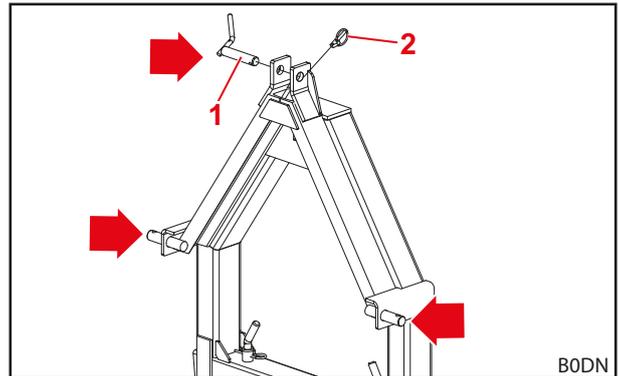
Punti di fissaggio per il montaggio sul lato posteriore del trattore
